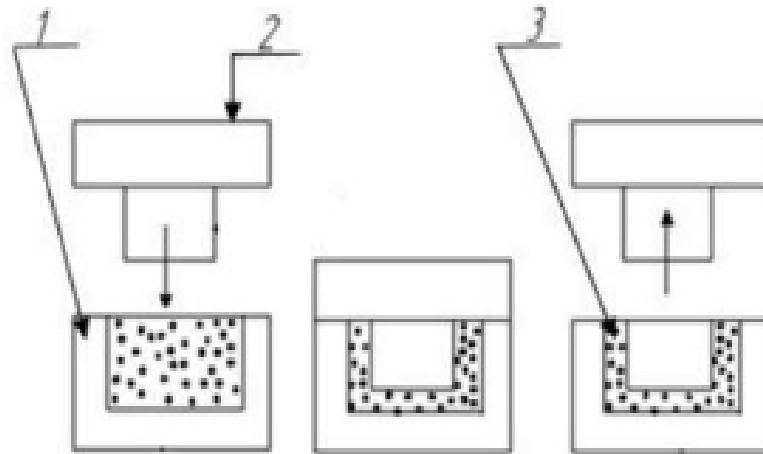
Пример литья композиционного сплава под давлением (штамповка): 1 – нижний штамп; 2 – верхний штамп; 3 – форма
